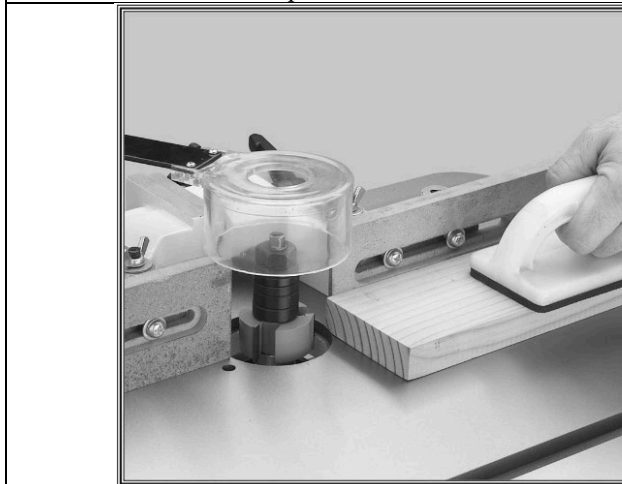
Используйте прорезиненное приспособление для удержания заготовки во время обработки.
